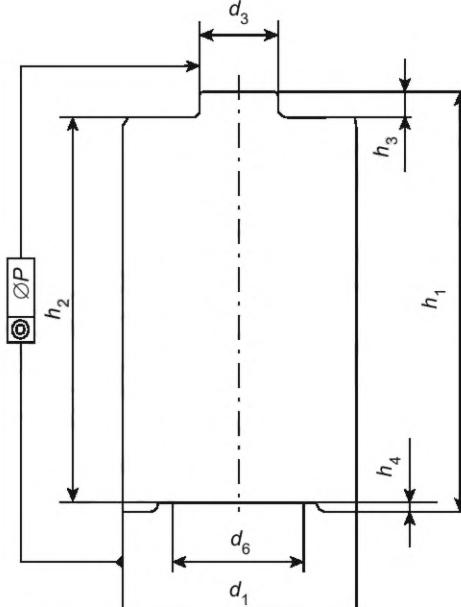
Габаритный чертеж LR20, R20P, R20S
